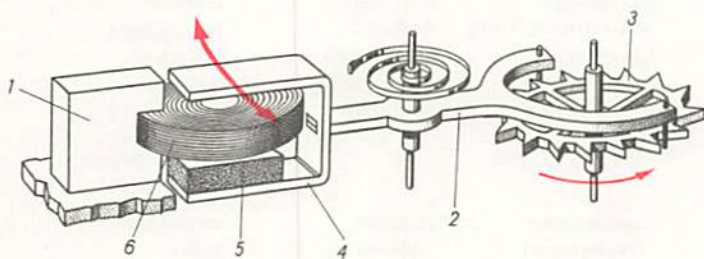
Unipolarer Wandler mit Winkelschritt und bewegtem Magnetsystem
